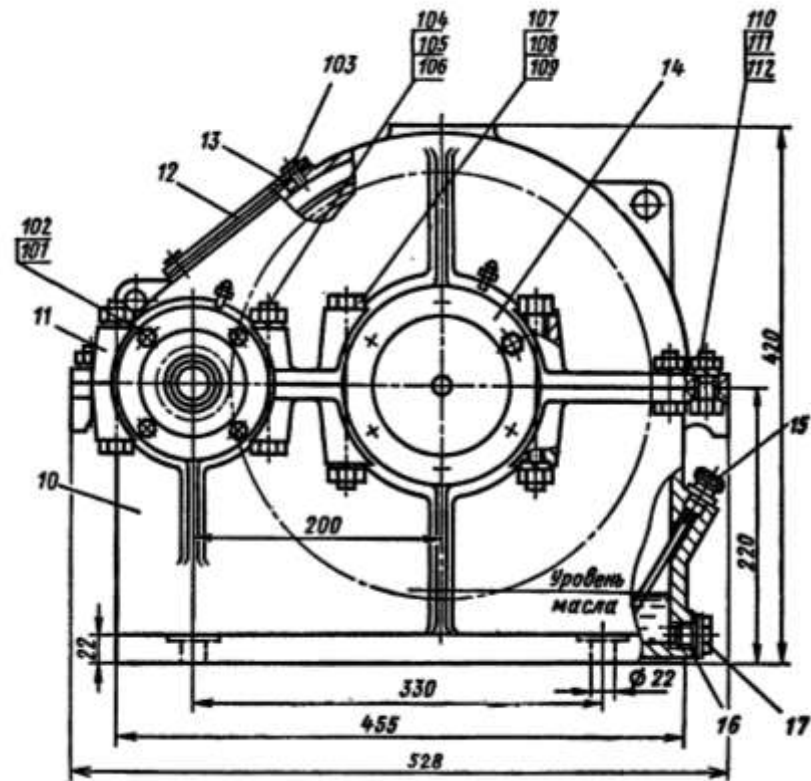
Цилиндрический одноступенчатый зубчатый редуктор.
